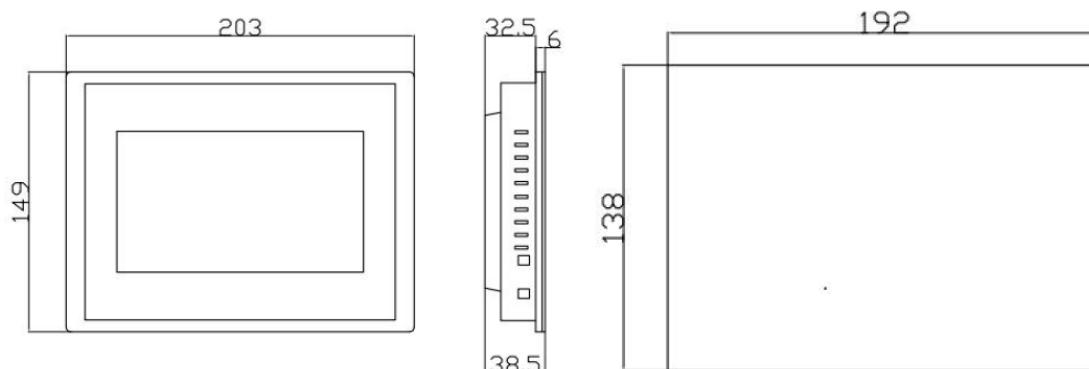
Dimensión de la IHM en la izquierda y recorte del tablero a la derecha
